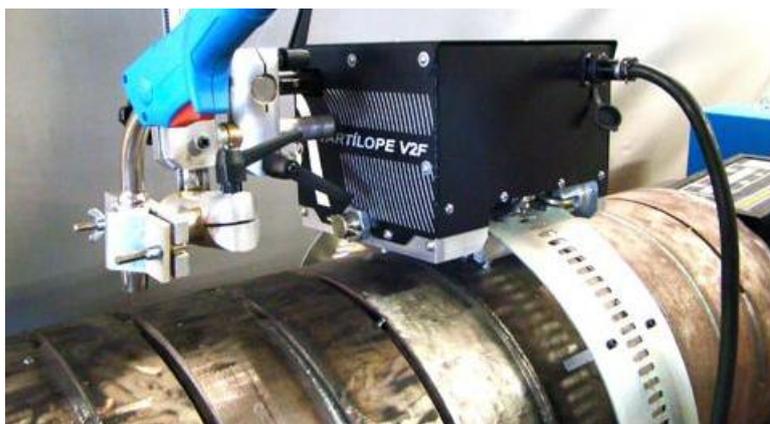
Manipulador de solda Tartílope V2F desenvolvido para soldagem orbital de tubos
